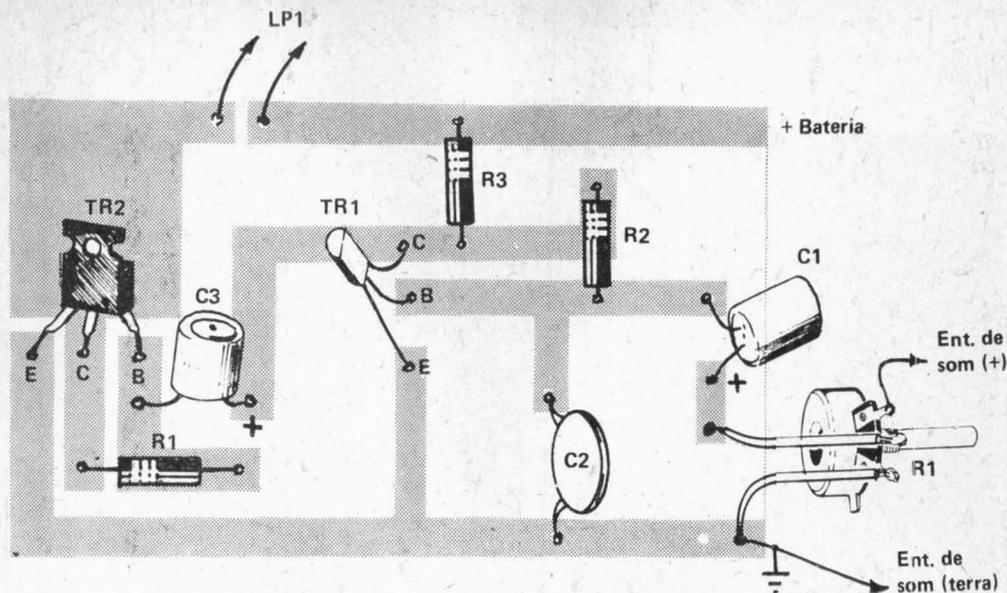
Disposição dos componentes sobre a plaqueta.
